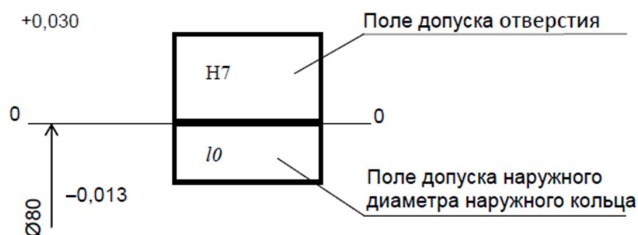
Схема полей допусков сопряжения отверстия корпуса и наружного кольца подшипника качения нормального класса точности
